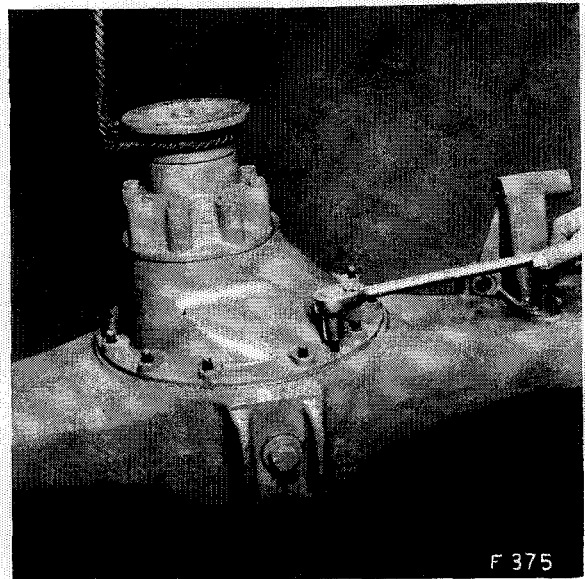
Eindrehen der Schrauben M10 zum Abdrücken der Antriebsgruppe aus dem Achskörper
